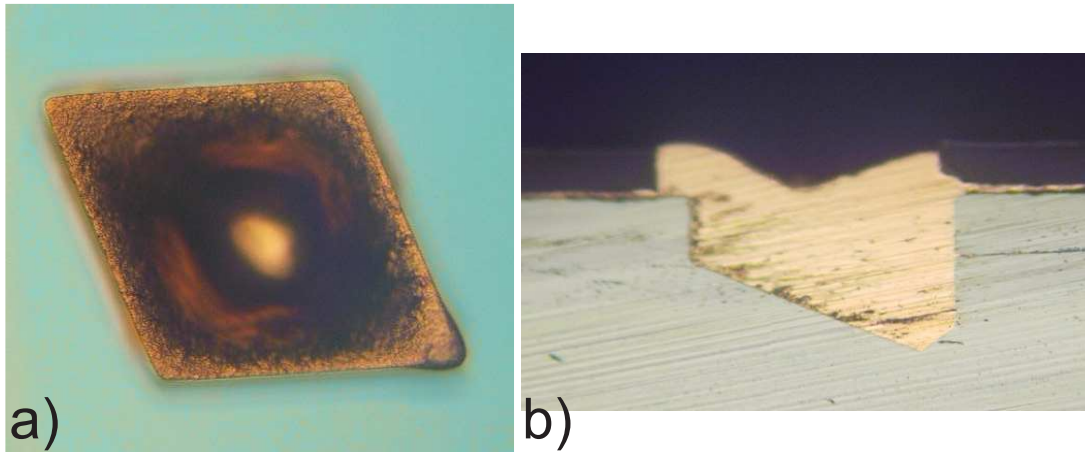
Mit Kupfer galvanisch aufgefüllte Rautenstruktur; Aufsicht (a), Querschnitt (b) [58]
